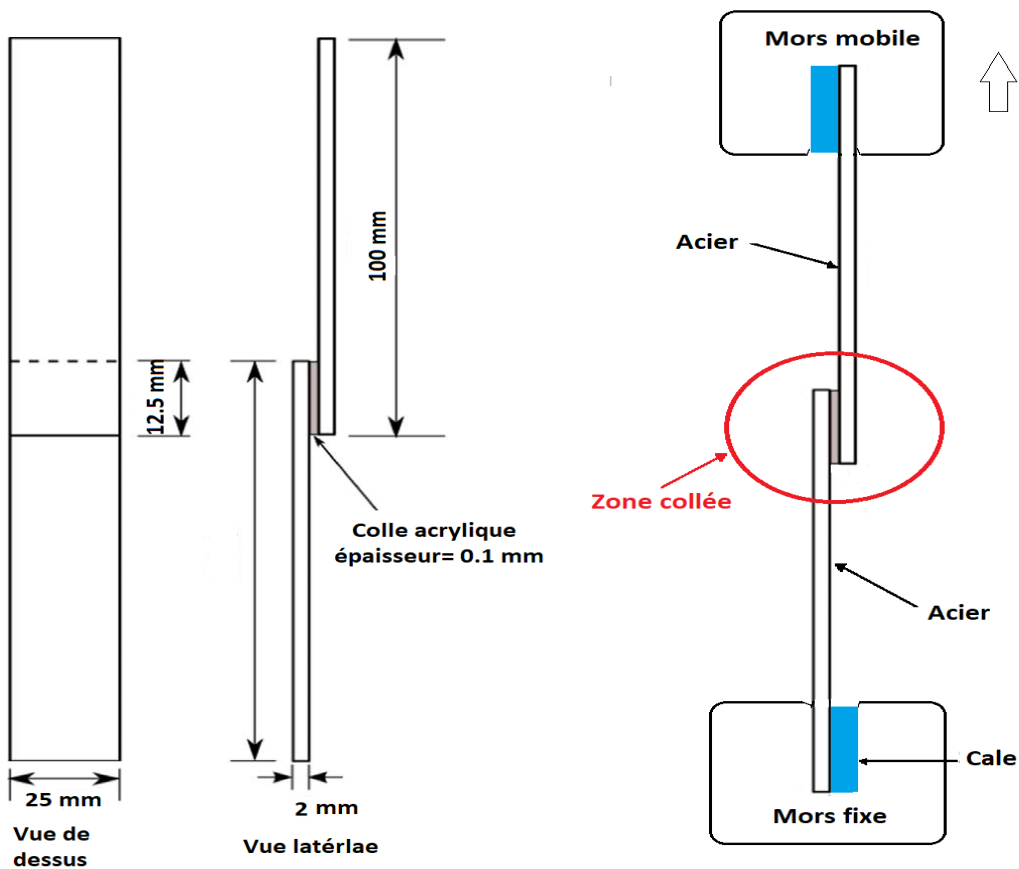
Essai de cisaillement à simple recouvrement- Collage SLJ en acier/acier.
